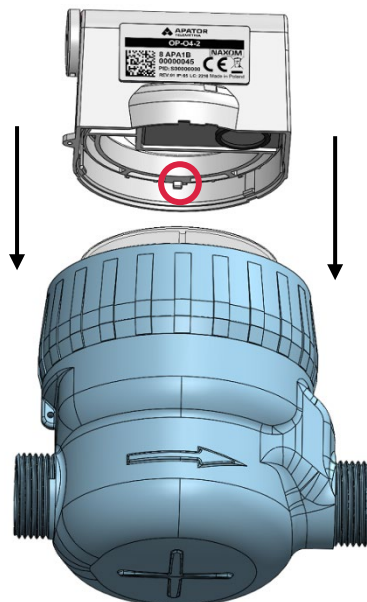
Ansicht des Wasserzähleraufsatzes OP-O4-2, vor der Montage auf dem Wasserzähler SV-RTK.
